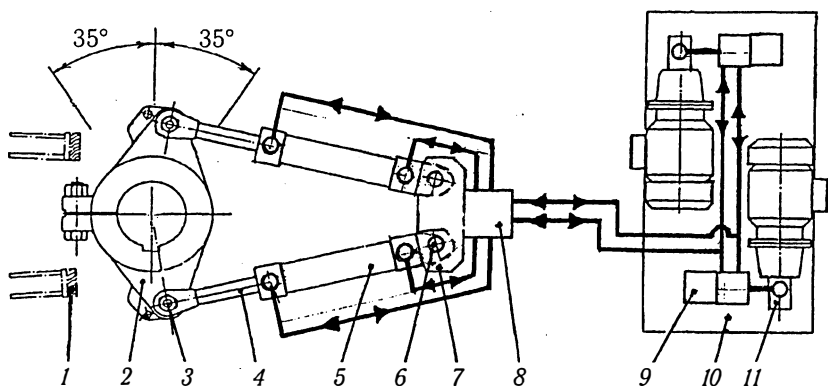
Компоновка поршневой ГРМ: 1 — механический упор, 2 — румпель, 3 — сферический подшипник, 4 — шток, 5 — цилиндр, 6 — подшипник, 7 — фундаментная опора, 8 — блок клапанов, 9 — фильтр, 10 — бак рабочей жидкости, 11 — насос
